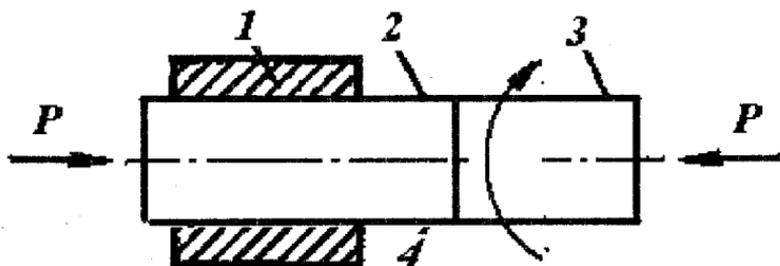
54. Схема зварювання тертям за взаємного тертя поверхонь заготовок:
